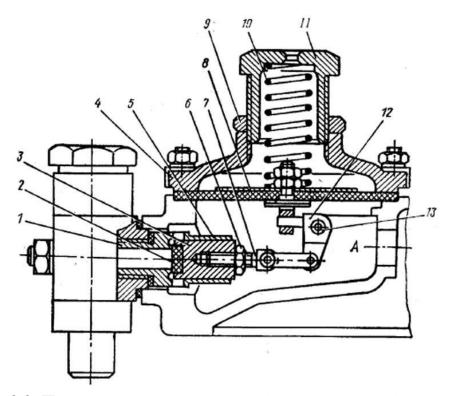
Первая ступень редуктора: А-полость первой ступени 1-седло клапана; 2- уплотнитель; 3-клапан; 4-крышка; 5-направляющая клапана; 6-контргайка; 7-винт; 8-диафрагма; 9-контргайка; 10-пружина; 11-регулировочная гайка; 12-рычаг; 13-ось.
